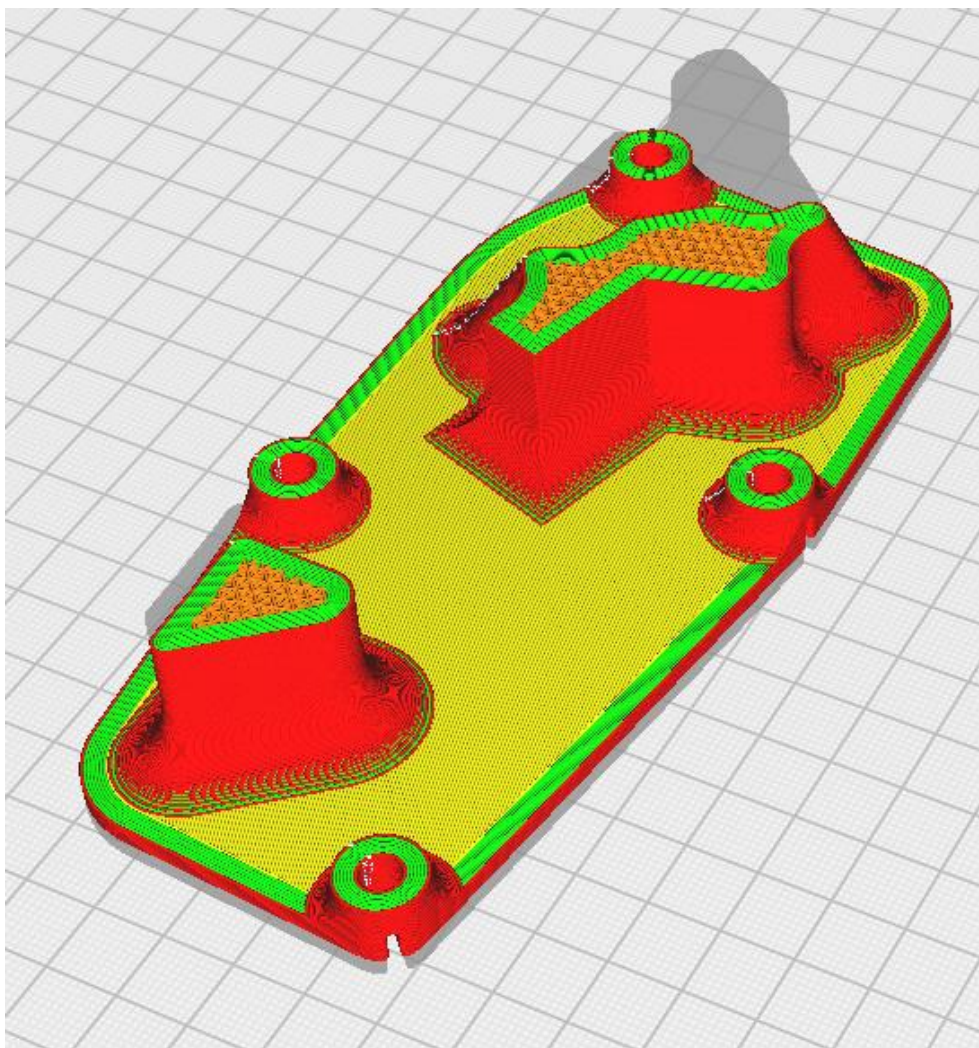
Vista módulo 2 del utillaje para pieza 3 en el laminador de Ultimaker Cura
